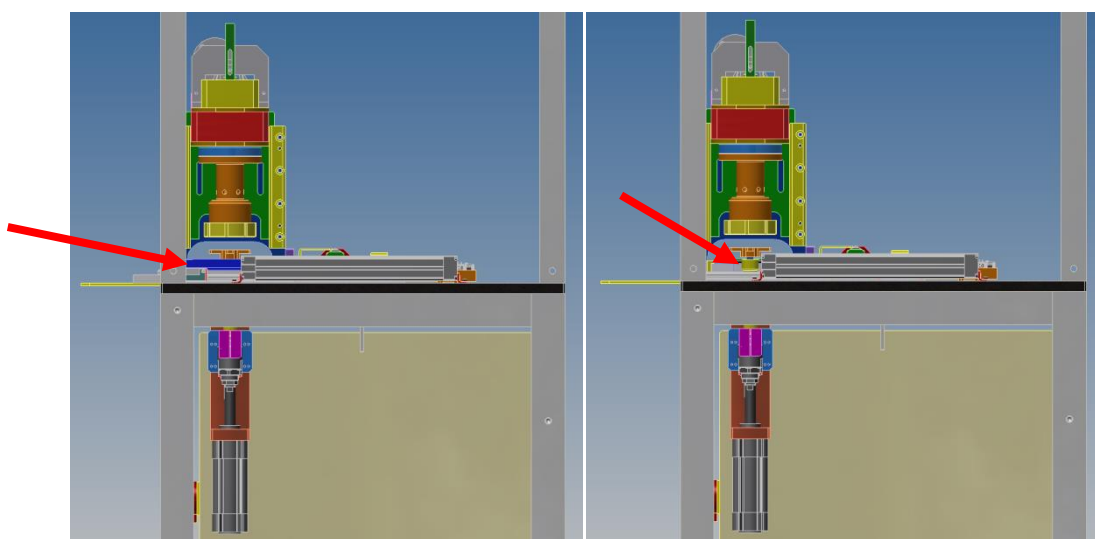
Máquina vista de perfil seccionada por el eje de la Cruz de Elevación.
